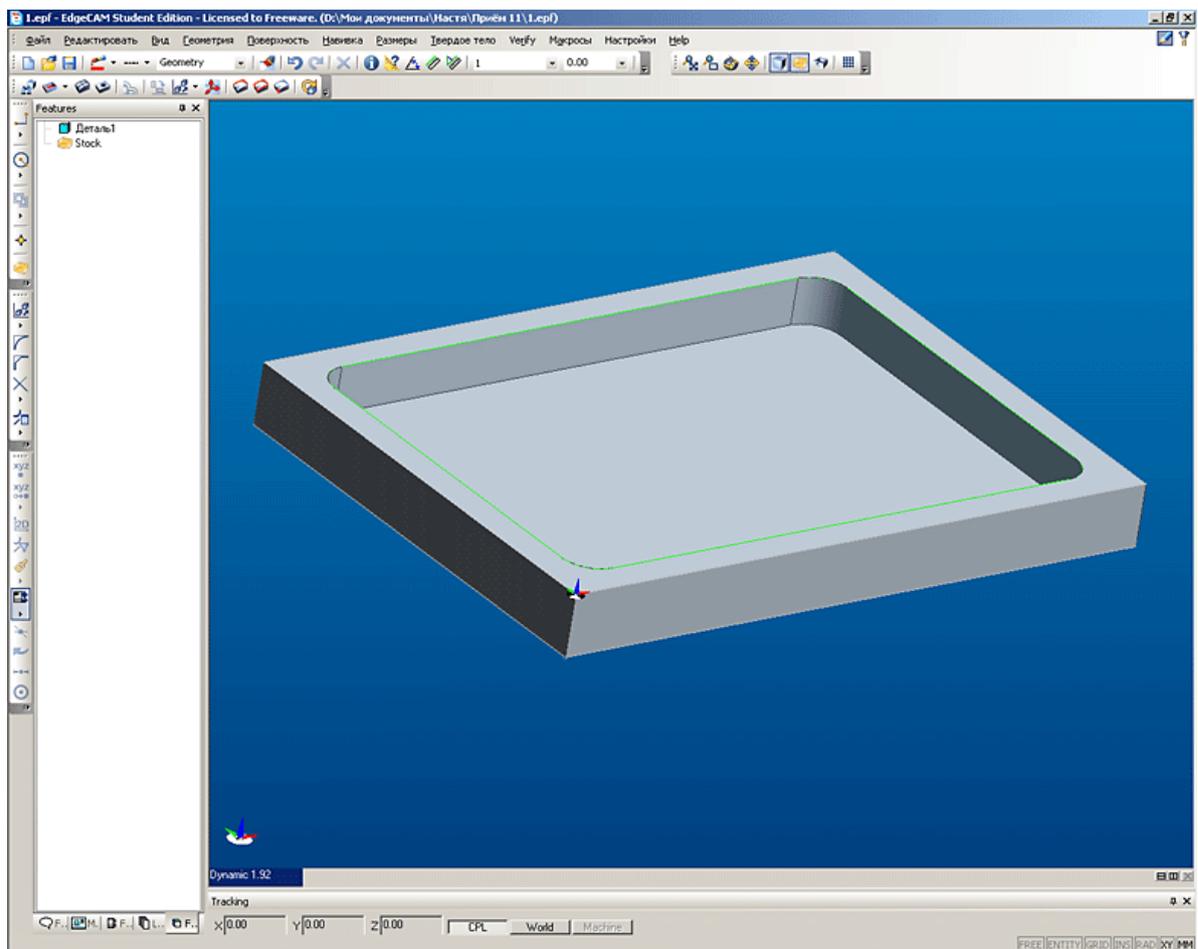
Edgесam. Деталь с созданной ПСК и заготовкой.
